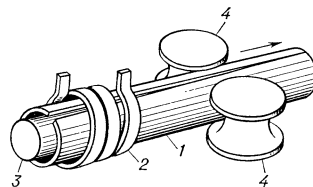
Схема высокочастотной сварки труб индукционным способом: 1 — труба; 2 — индуктор; 3 — сердечник; 4 — обжимные ролики.
